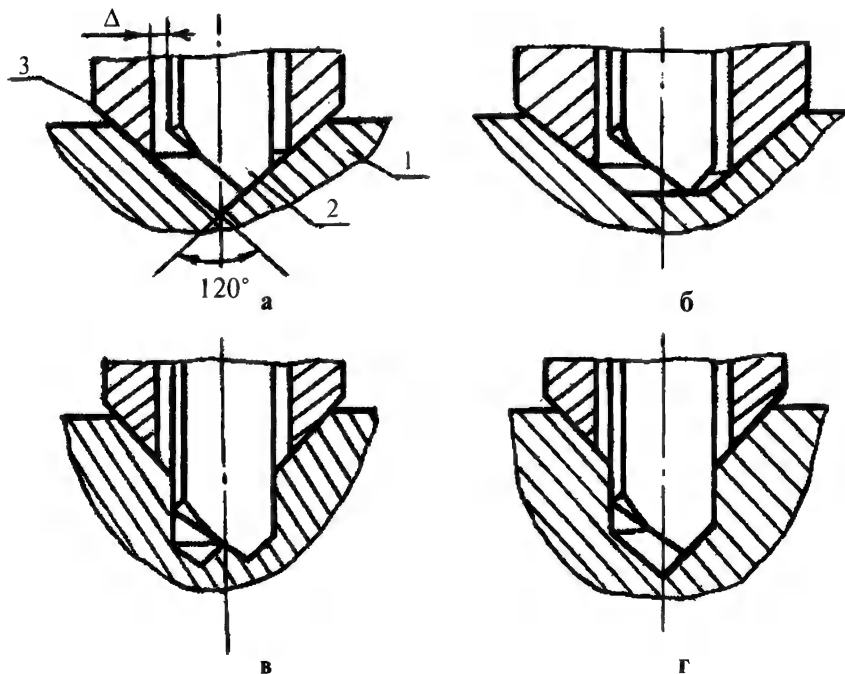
Формы зацентровки заготовок: а - конусная, б - усеченно-конусная, в - по форме сверла, г - стандартная; 1 - деталь, 2 - сверло, 3 - пустотелый центр
